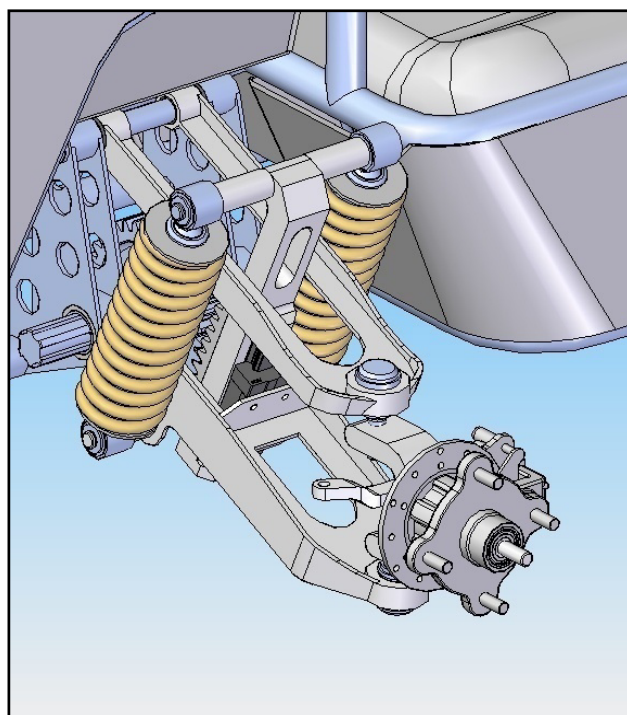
třetí varianta instalace pružící a tlumící jednotky
